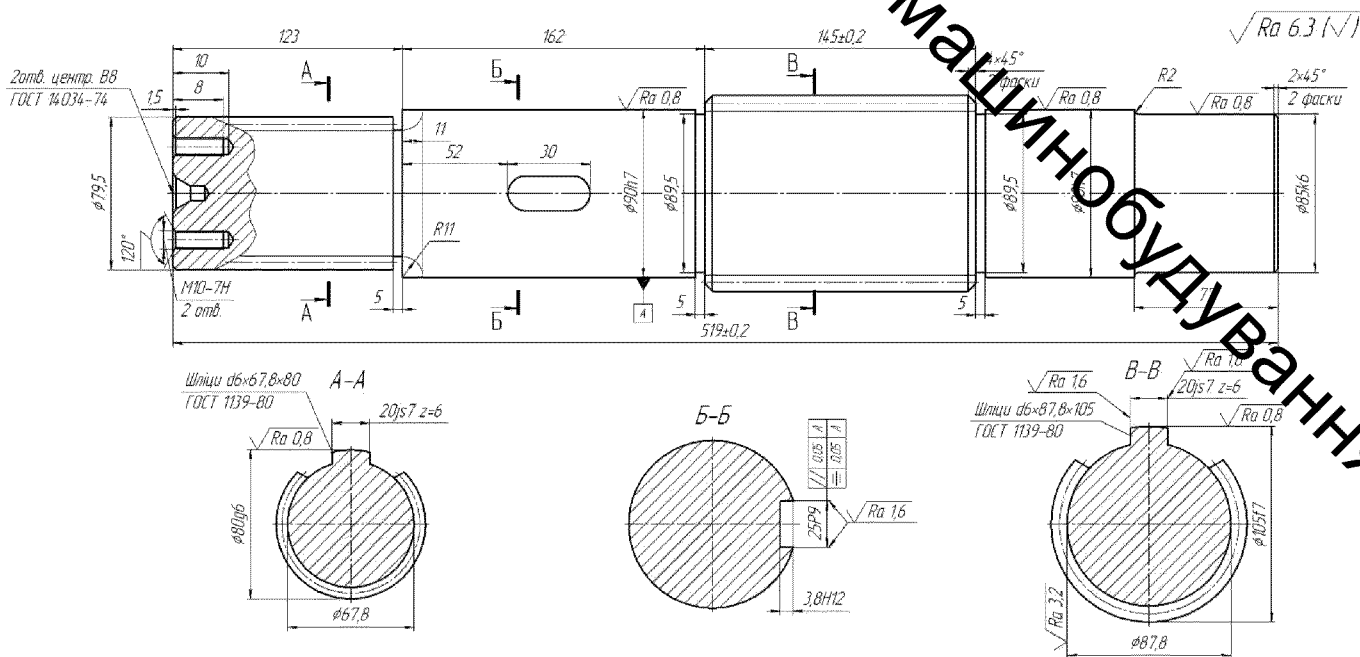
Робочий кресленик деталі «Шліцьовий вал»
